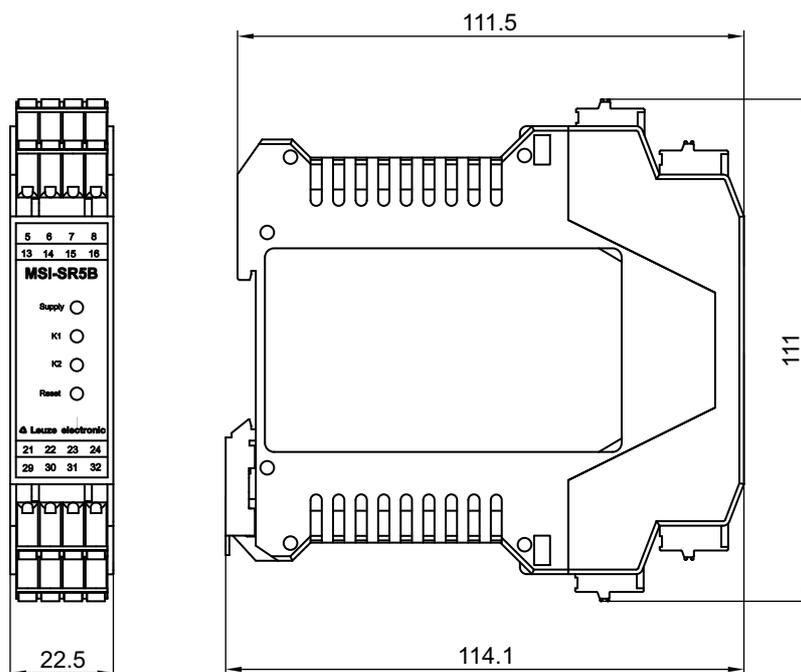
Dimensioni dell'MSI-SR5B-02
